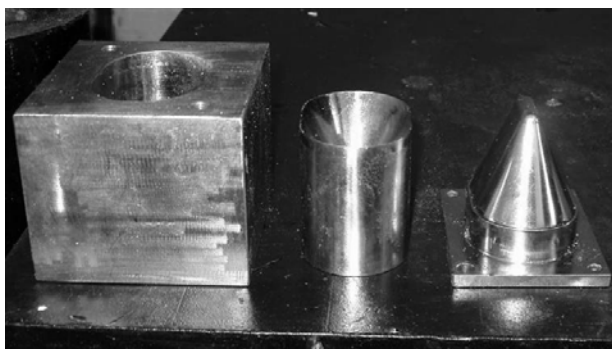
Внешний вид пресс-инструмента для изготовления зарядов
